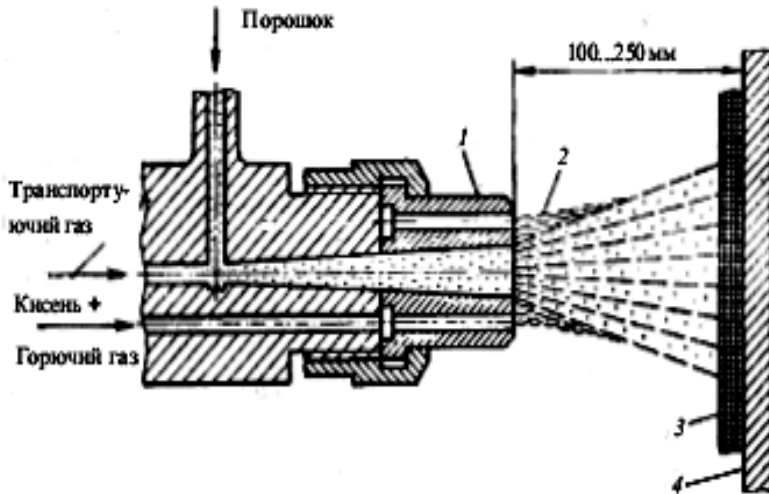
Схема газополуменевого напилення порошкового матеріалу.
